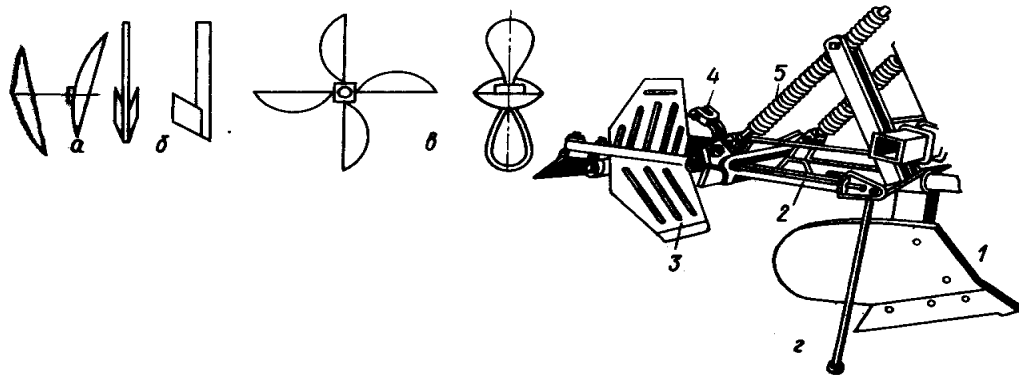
Робочі органи машин і знарядь для обробітку ґрунту, схильного до водної ерозії: а- ексцентричні диски лункоутворювача; б-ніж щілиноріза; в- ротор переривача борозни; г – пристрій до плуга для утворення переривчастої борозни: 1-корпус із скороченою полицею; 2-поводок; 3-крильчатка; 4-упорний важіль (привод від опорного колеса); 5-штанга з пружиною
